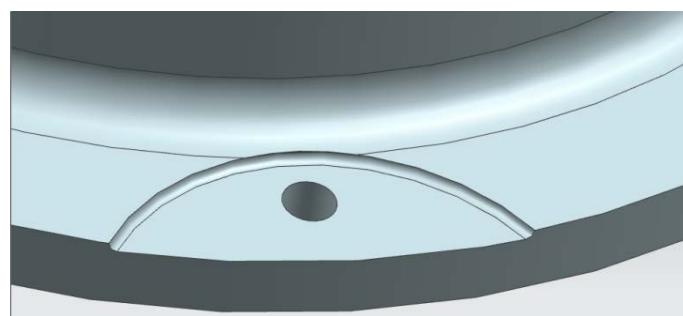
3D модель корпуса с выполненными скруглениями
